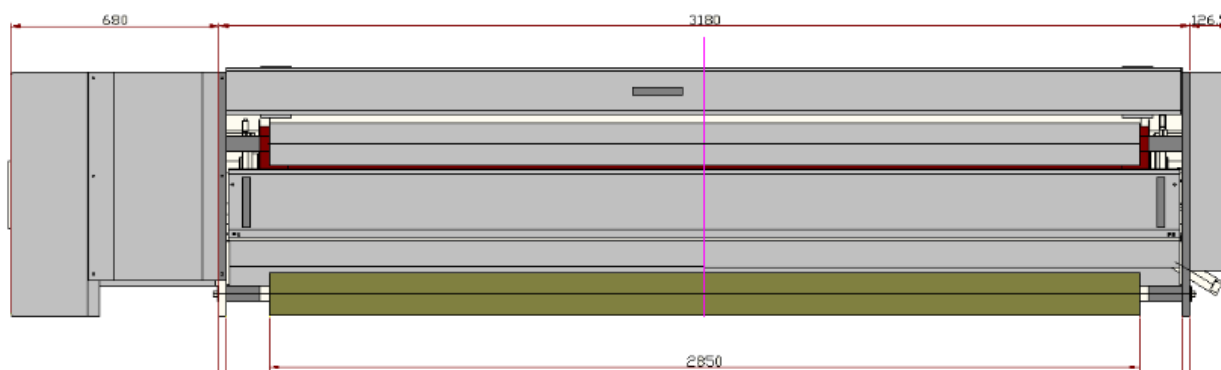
Plano mecánico frontal y dimensiones (fuente: manual de usuario Carteam)
